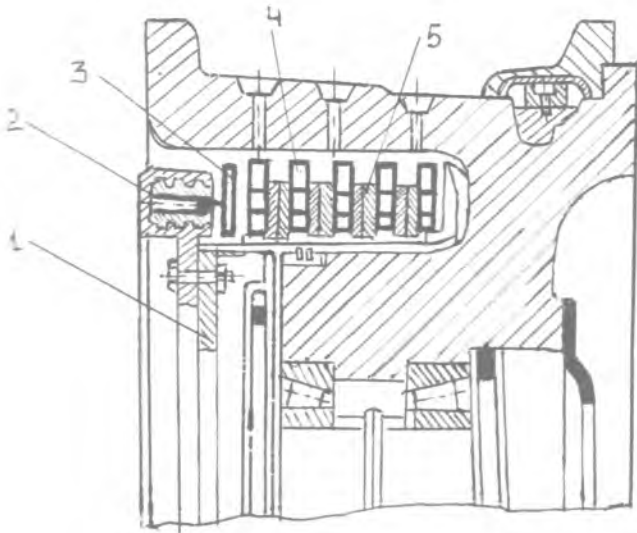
Дисковый тормоз: 1 - корпус, 2 - цилиндр, 3 - нажимной диск, 4 - подвижный диск; 5 - неподвижный диск,
